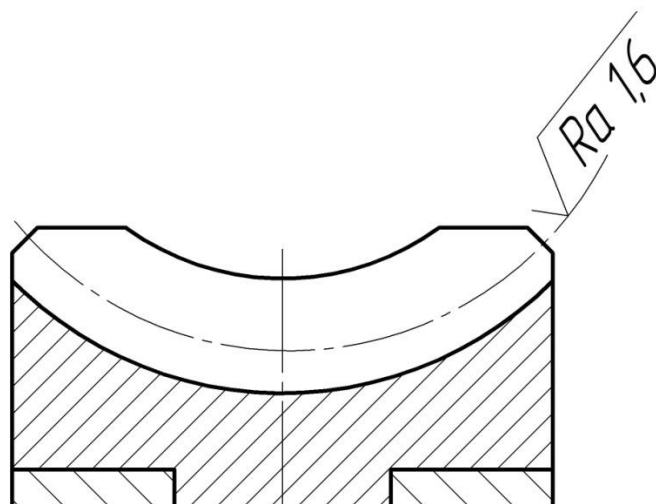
Обозначение шероховатости рабочей поверхности зубьев червячного колеса
